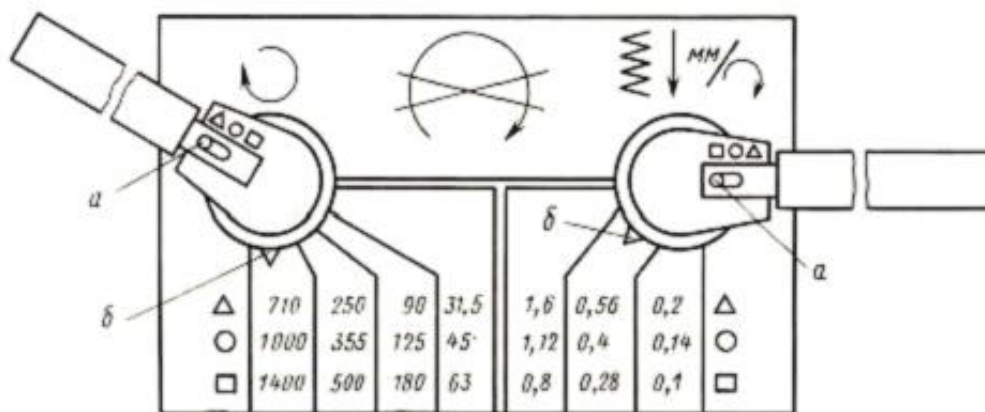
Загальний вигляд блоку керування коробкою швидкостей і коробкою подач
